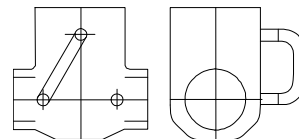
Закрытый патрубок для защиты от избыточного давления
